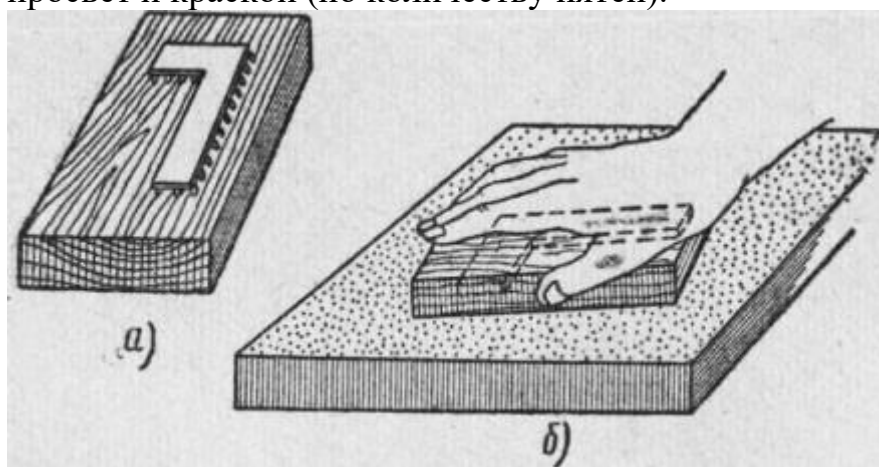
Притирка плоских сторон угольника: а — угольник закреплен на деревянном бруске, б — прием притирки угольника на плите
